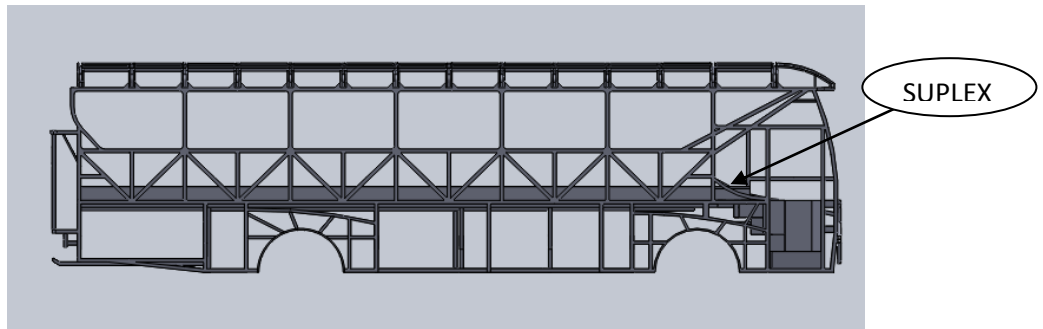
Vista Lateral de la Estructura Metálica de una Carrocería
